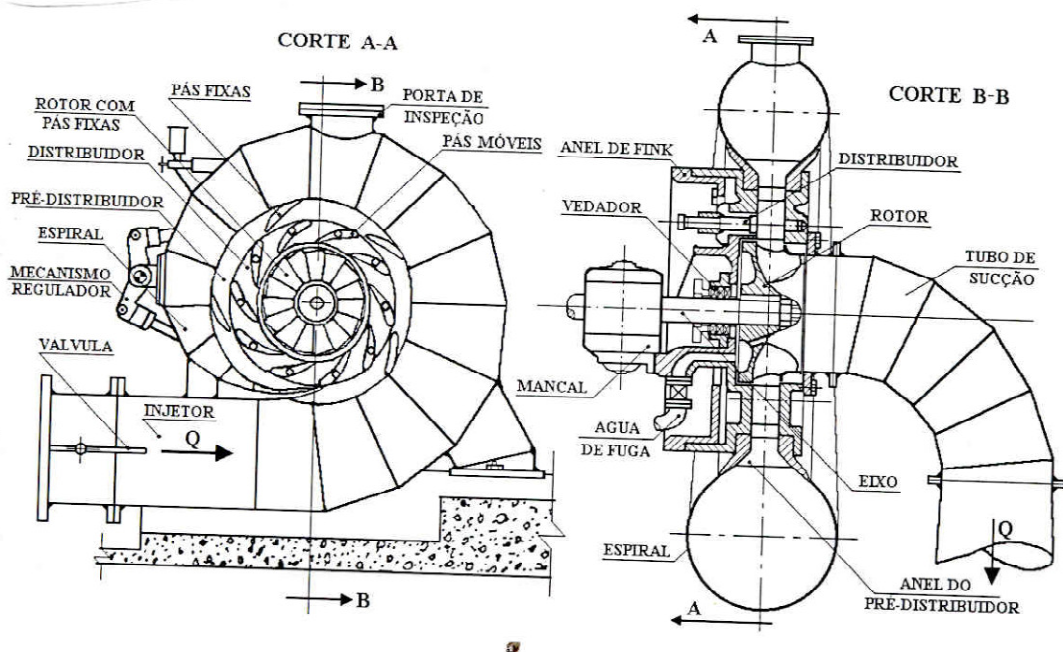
Turbina de ação (TH Francis de eixo horizontal e caixa espiral de chapa soldada).
